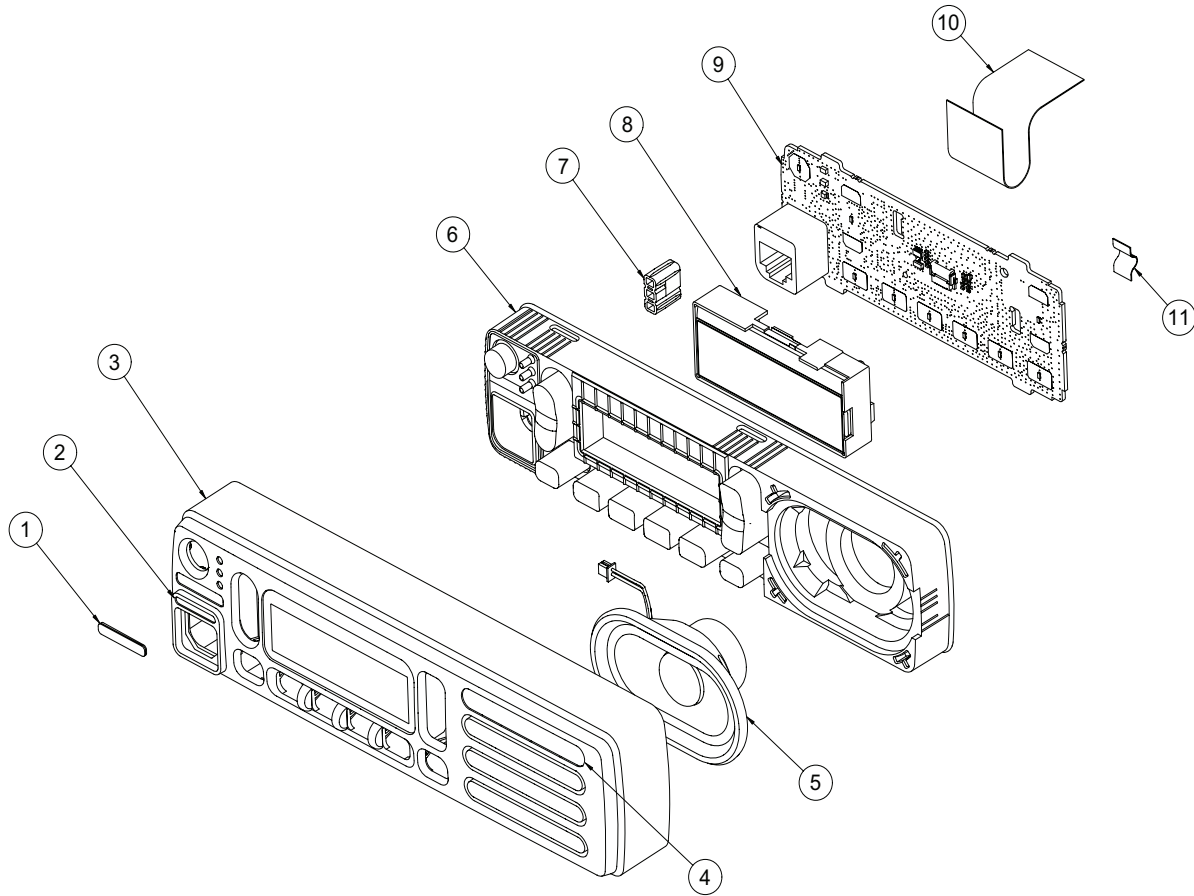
Vista del despiece del cabezal de la pantalla alfanumérica
